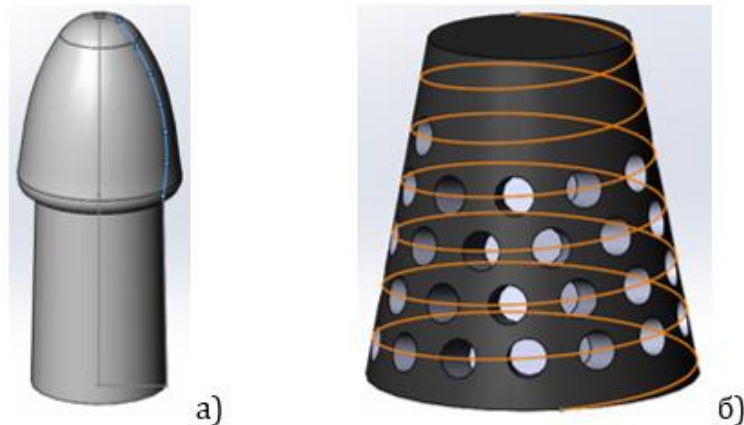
Особливості конструкції зубчатих конусних коліс: а – утворення робочої поверхні зубця; б – схема розміщення отворів для встановлення зубців
